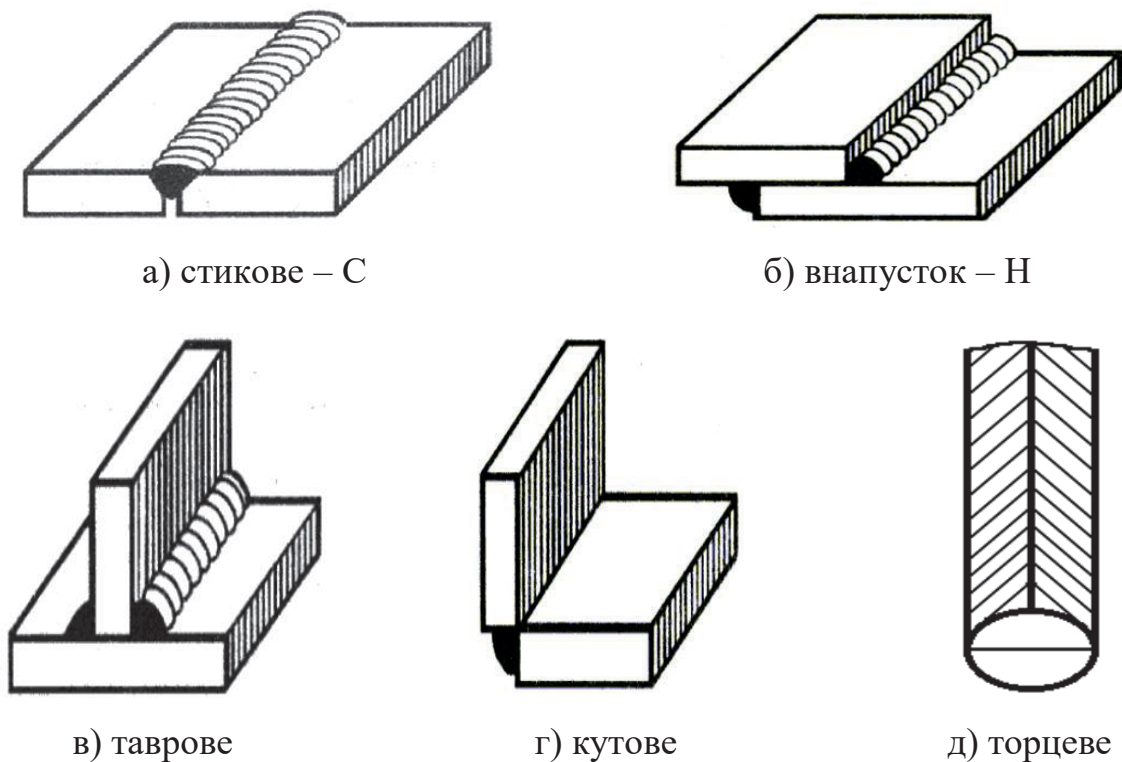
Основні види конструктивних з'єднань деталей зварюванням
